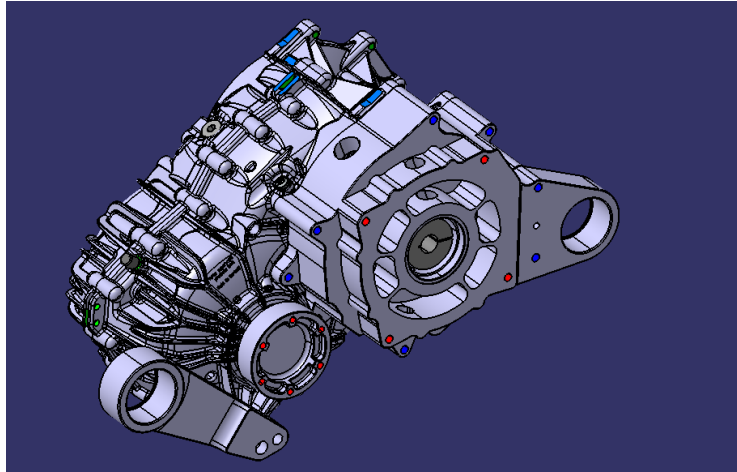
Adapterplatte MOLABO-Motor zu Getriebe am V1
